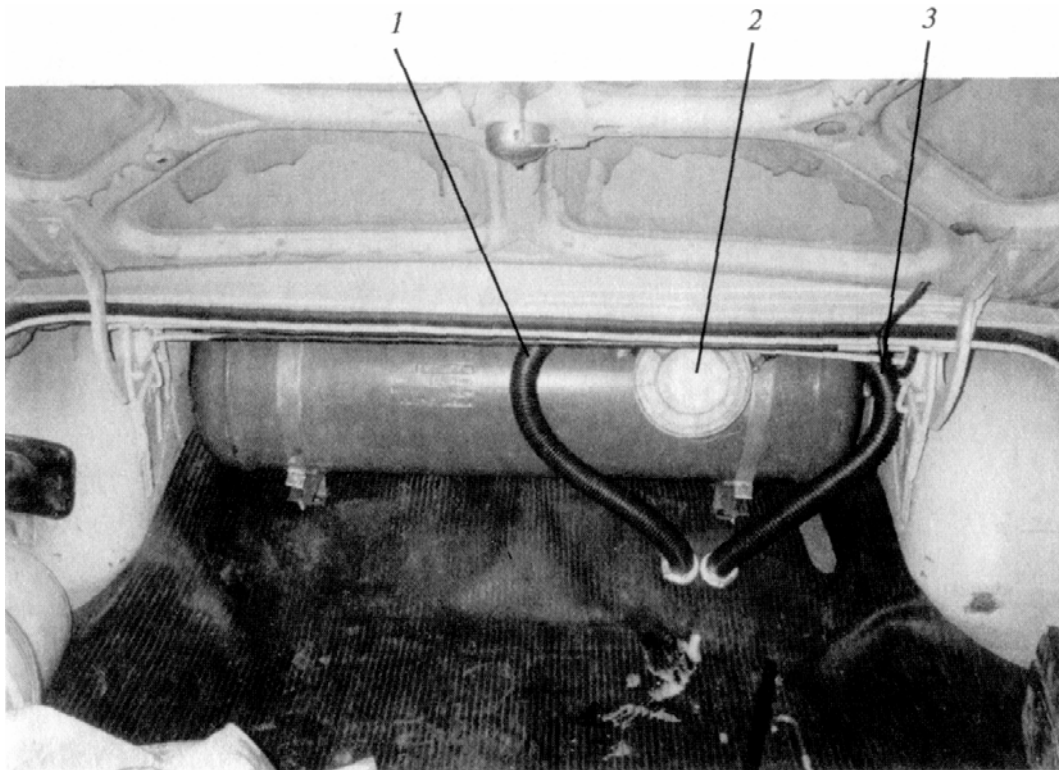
Расположение баллона ГСН с арматурой в багажнике:
